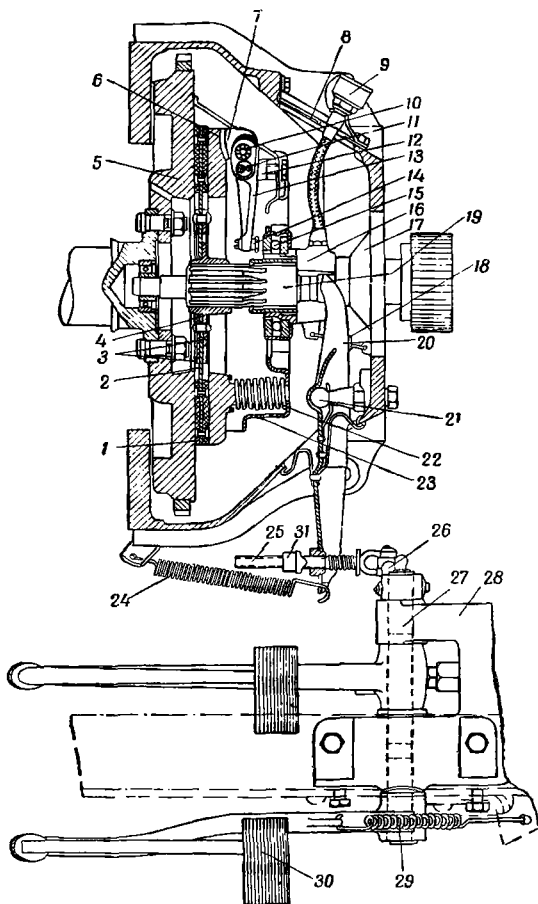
Одподишковое сцепление автомобиля ГАЗ-51
